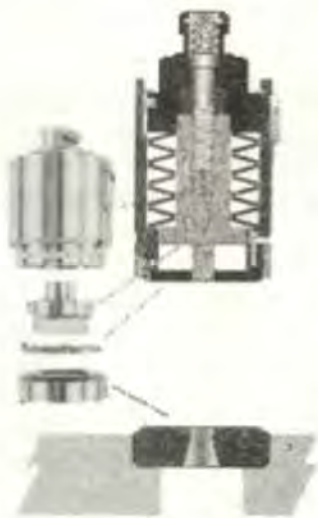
Esquema de un cartucho para el montaje del punzón de Mate Punch & Die Co.
